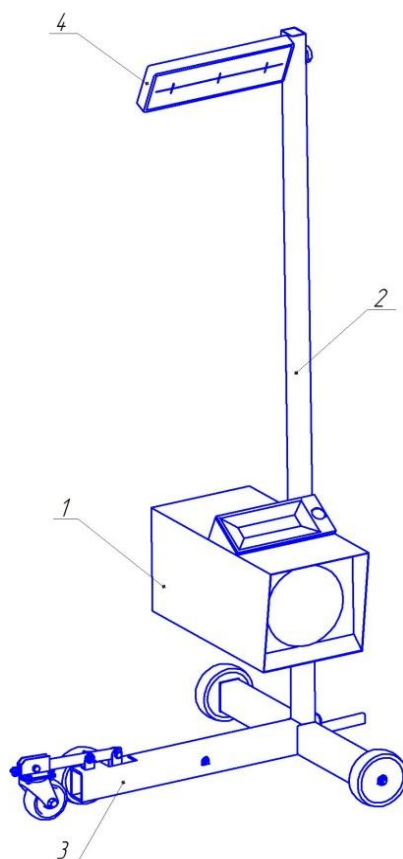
Общая компоновка устройства для контроля и регулировки света фар
